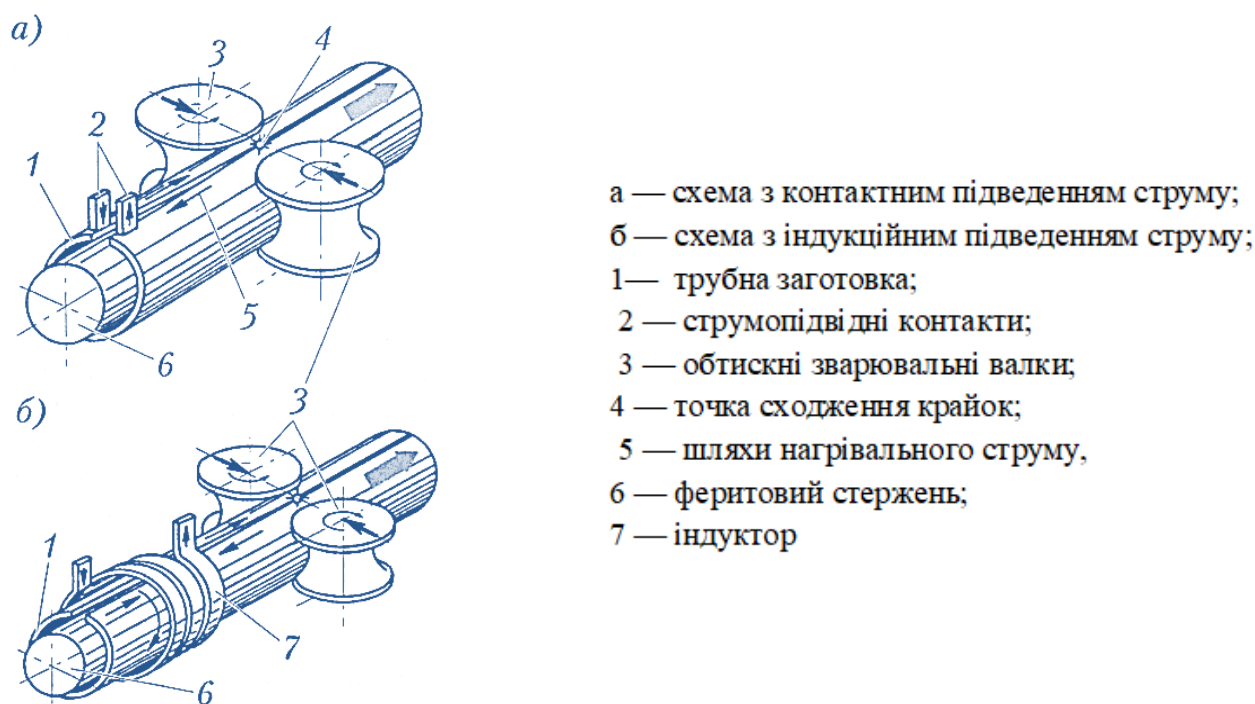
Схема процесу високочастотного зварювання труб [6]
